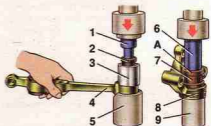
Запрессовка резинометаллических шарниров: рычага подвески и кронштейна крепления растяжки: 1 – оправка; 2 – резинометаллический шарнир; 3 – направляющая втулка; 4 – рычаг подвески; 5 – опорная втулка; 6 – оправка; 7 – резинометаллический шарнир; 8 – кронштейн крепления растяжки; 9 – опорная втулка; А – поверхность с маркировкой шарнира
